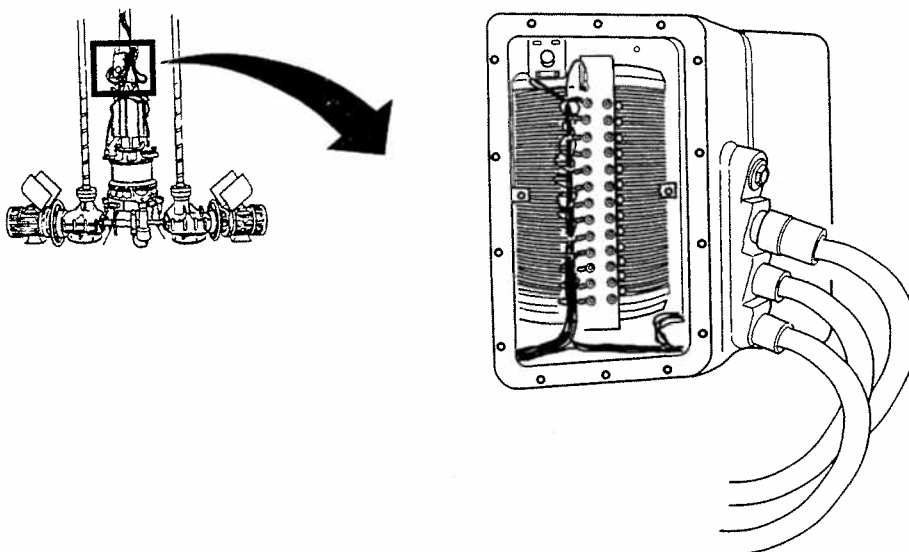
Släpringsenhet. Inspektionsluckan demonterad.
